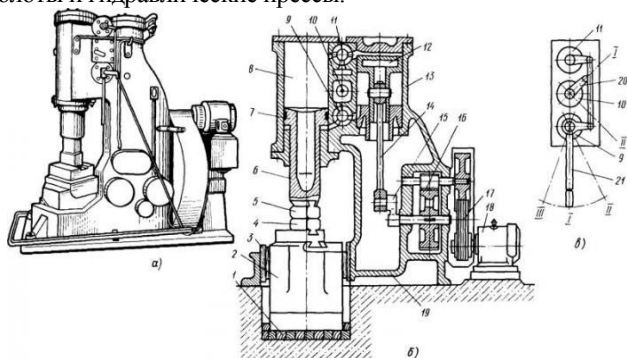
Пневматический ковочный молот: а - общий вид, б устройство, в - кинематическая схема; 1 - брусья, 2 - шабот, 3 - клинья, 4, 5 – нижний и верхний бойки, 6 - шток, 7, 12 - поршни, 8, 13 - рабочий и компрессорный цилиндры, 9 ... 11 - краны управления, 14 - шатун, 15 - кривошипный вал, 16 - редуктор, 17 - ременная передача, 18 - электродвигатель, 19 - станина, 20, 21 рукоятки управления
